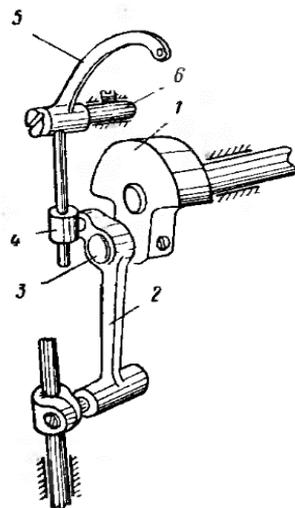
Кулисно-рычажный механизм нитепритягивателя
